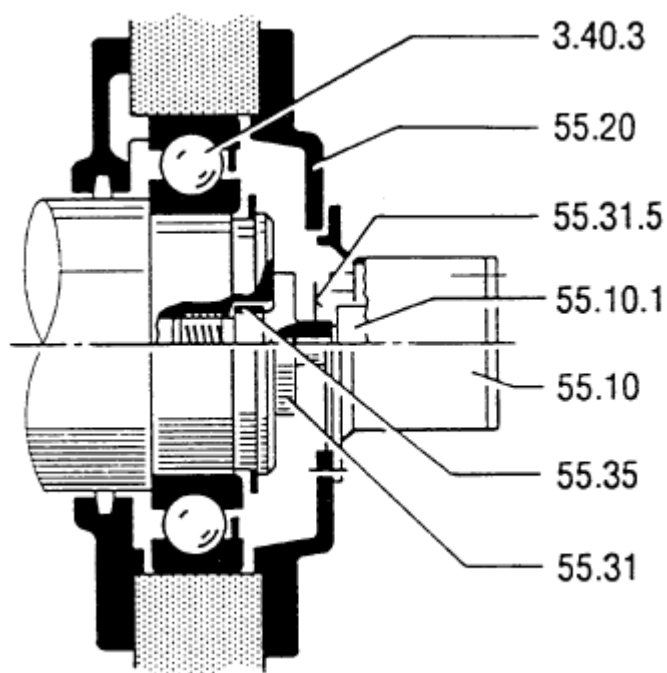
Transmissor de rotações para montagem suspensa para alturas de eixo de 180 a 630
